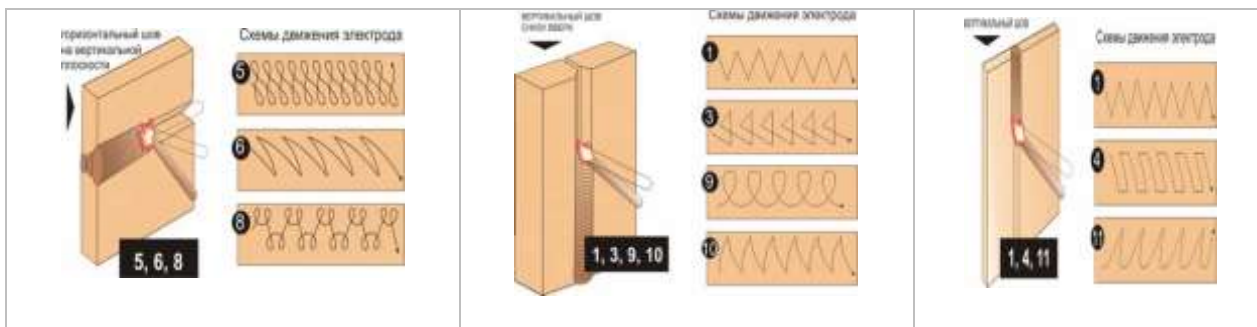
Схемы движения электрода при сварке горизонтальных и вертикальных швов
